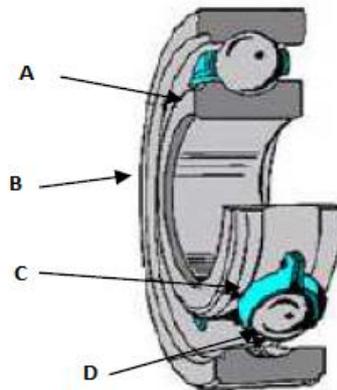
Partes del rodamiento de un motor. [22]
